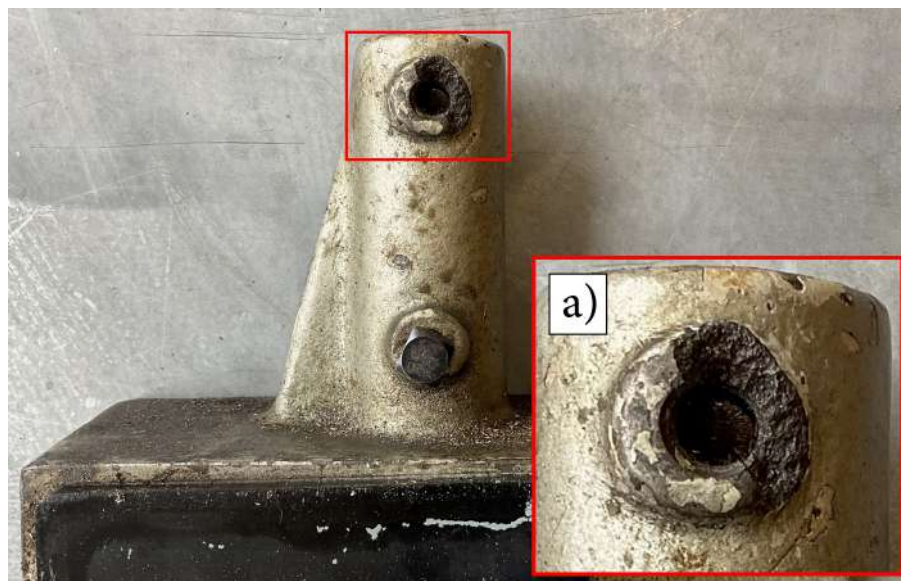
Suporte para motor 6.050: a) Vista de pormenor do defeito.
